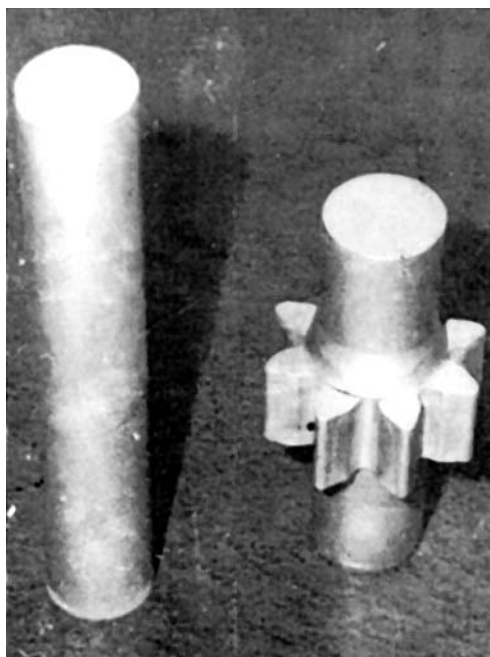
Заготовка и поковка шестерни с зубом, отштампованная на прессе Ф3134
